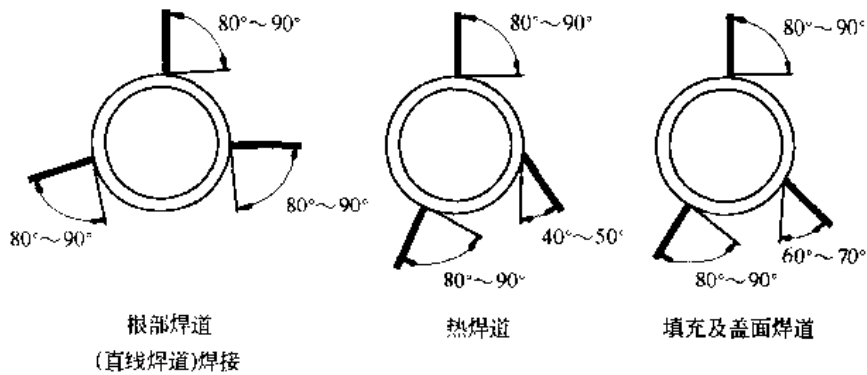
不同焊道焊接时推荐的焊条角度
